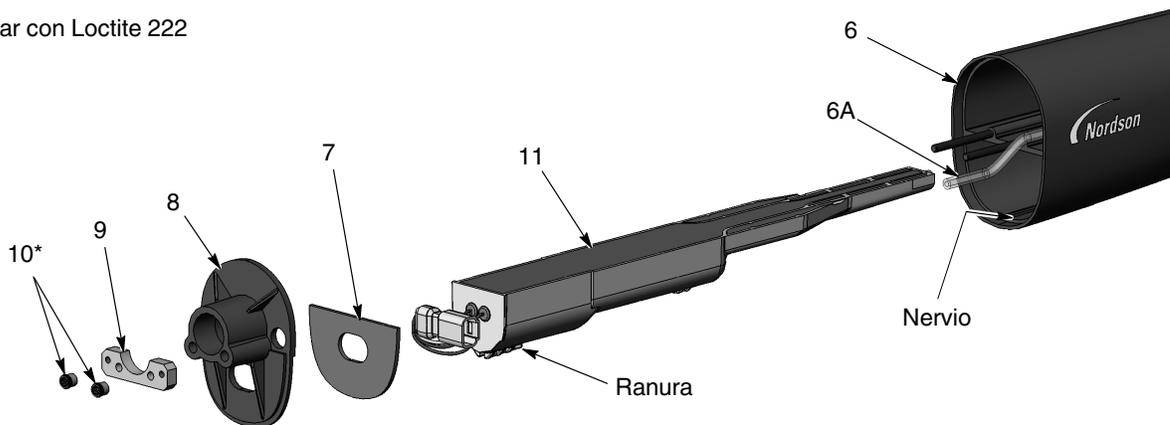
Desmontaje de la pistola de montaje en tubo 4 de 5
